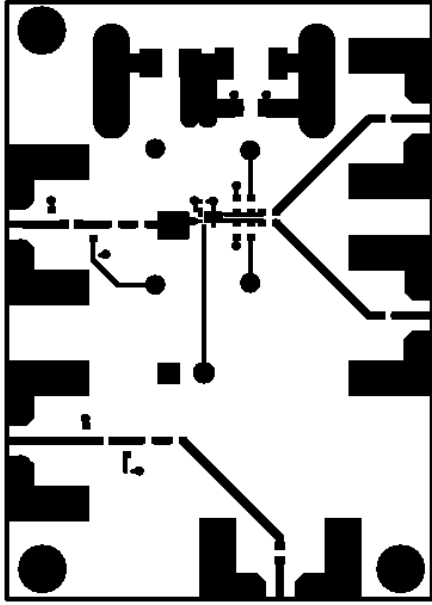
MAX3744/MAX3745 评估板 PCB 布线
